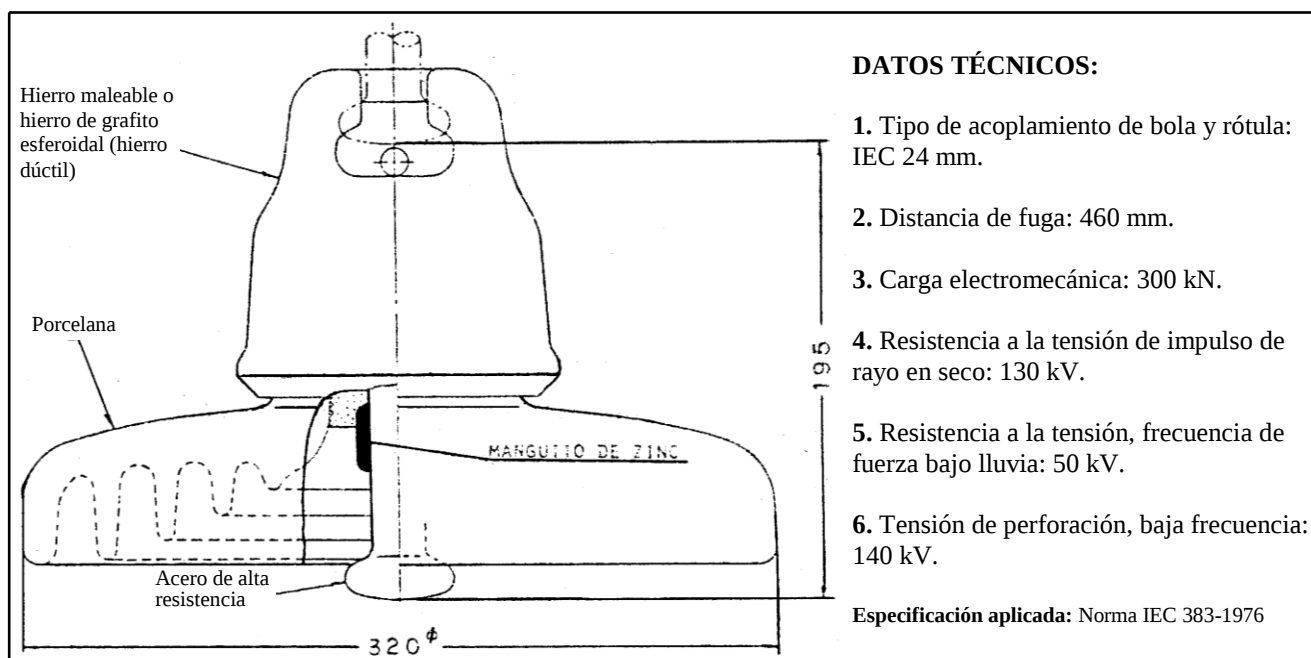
Aislador NGK de amarre para el diseño en zonas de baja o alta contaminación (CA-590).
